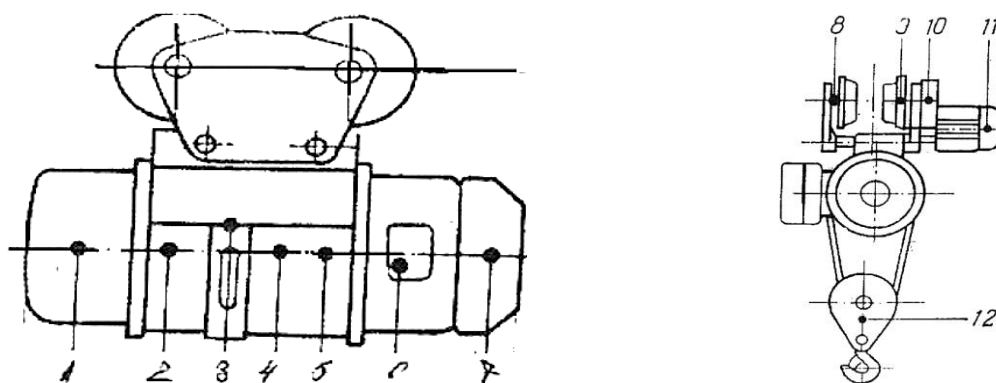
Схема электротельфера: 1 – планетарный редуктор; 2 – кожух; 3 – ограничитель подъема груза; 4 – барабан; 5 – канат; 6 – электродвигатель; 7 – тормоз; 8 – ось колес; 9 – колесо; 10 – редуктор механизма передвижения; 11 – электродвигатель механизма передвижения.
